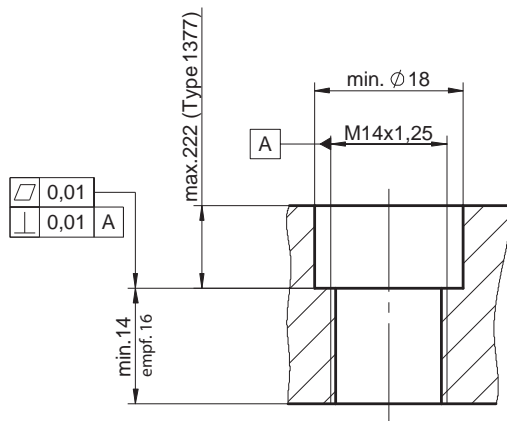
Bündig eingebauter Sensor. Bohrungsdurchmesser gemäss Montagewerkzeug
